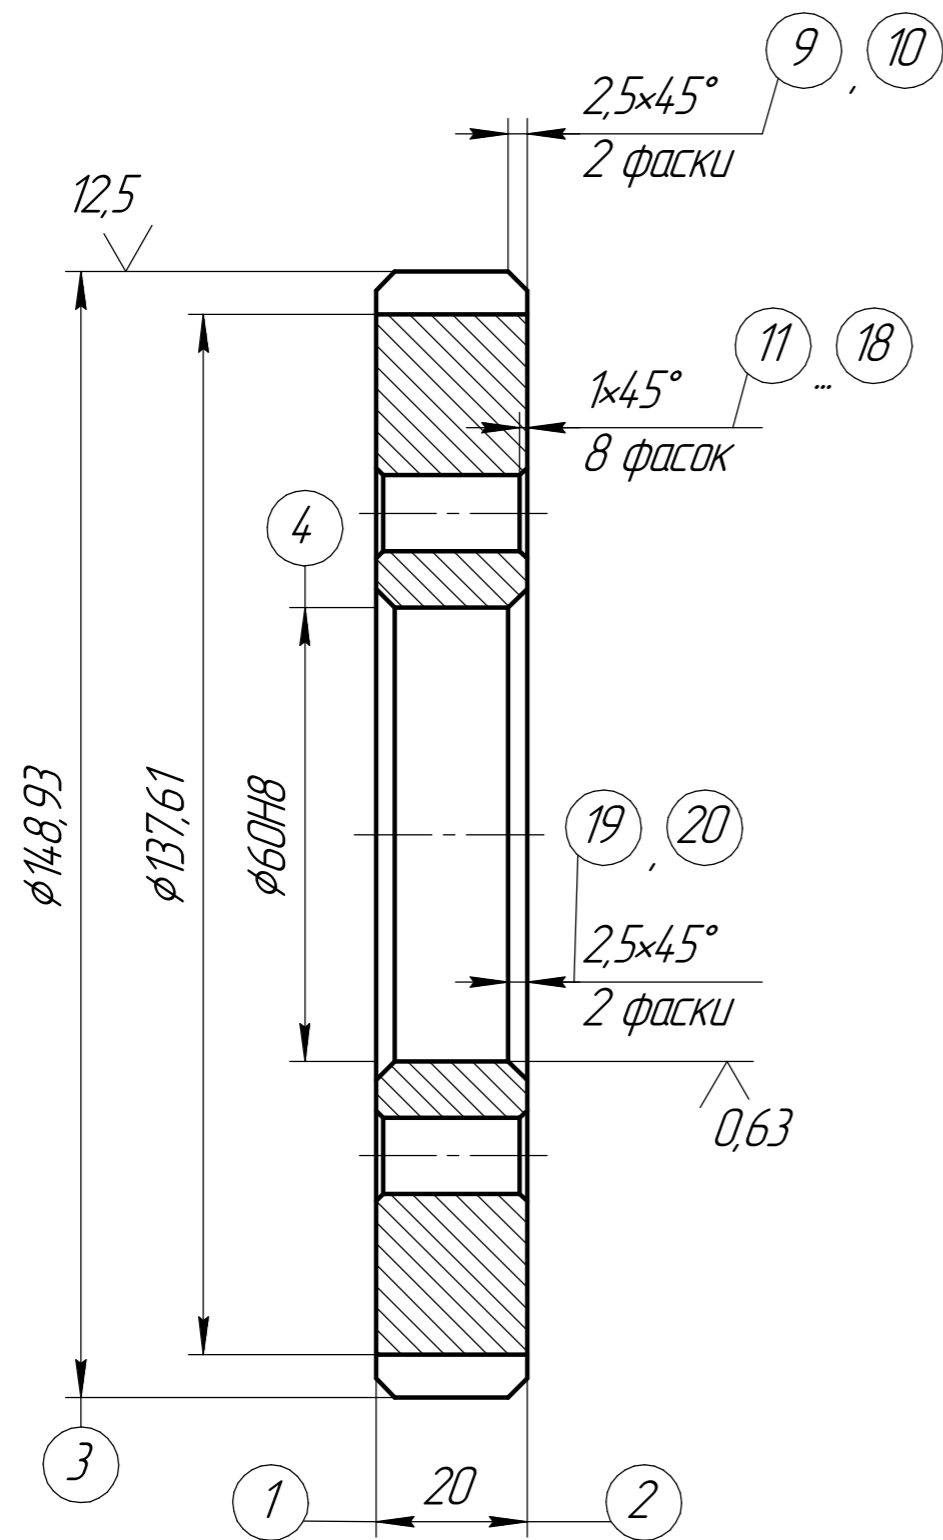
Ескіз деталі з номерами поверхонь
